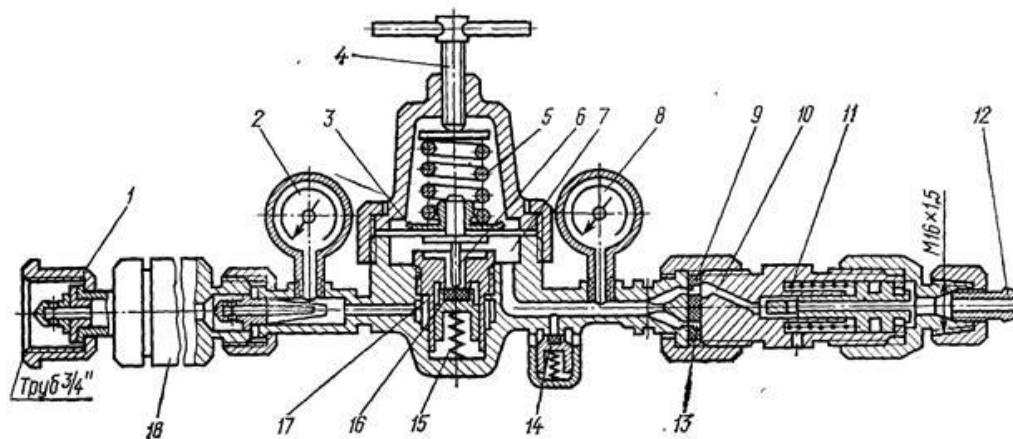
Схема газового редуктора У-30 для углекислого газа 1 — нажимная гайка, 2, 8 — манометры, 3 — мембрана, 4 — регулировочный винт, 5, 15 — пружины, 6 — игла, 7 — камера низкого давления, 9, 13 — калиброванные отверстия, 10 — канал, 11, 16 — запорные клапаны, 12 — штуцер, 14 — предохранительный клапан, 17 — седло, 18 — подогреватель газа.
